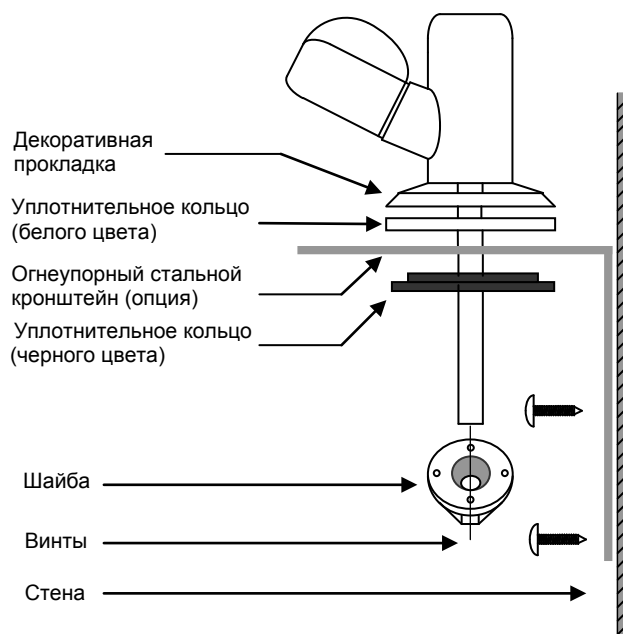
Установка дополнительного крана на стену при помощи стального кронштейна.
